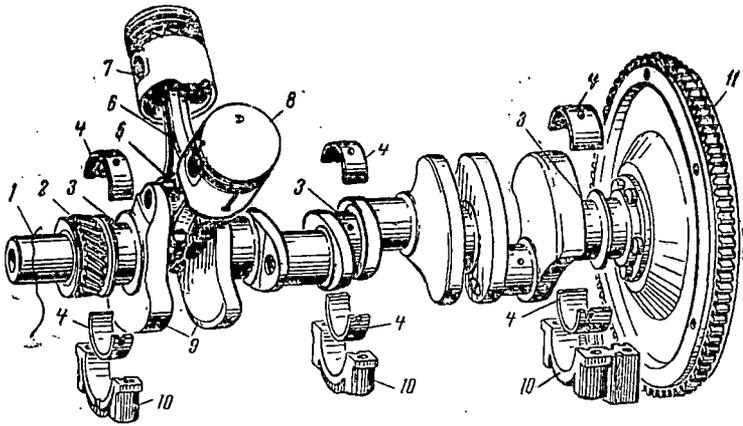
Коленчатый вал и поршневая группа двигателя ЗИЛ-130:
